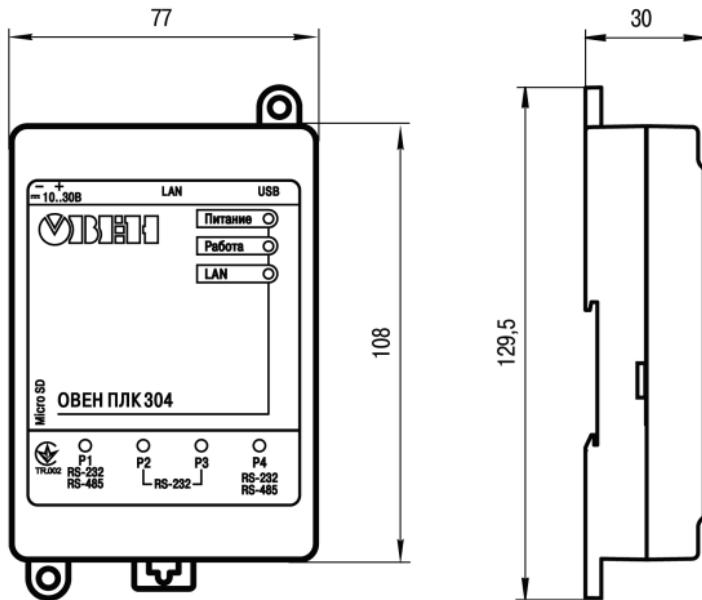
Габаритные размеры ОВЕН ПЛК304
